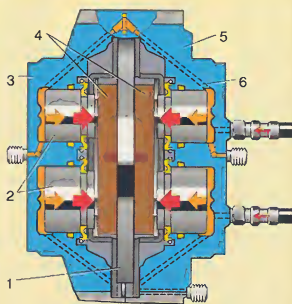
Механизм оппозитного типа: 1 — диск; 2 — поршни; 3 и 5 — половинки корпуса; 4 — колодки; 6 — соединительные каналы.
